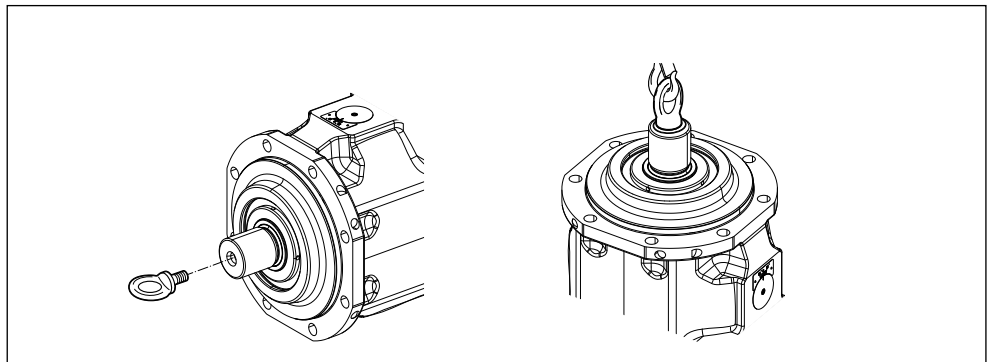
Befestigung der Ringschraube in der Triebwelle
